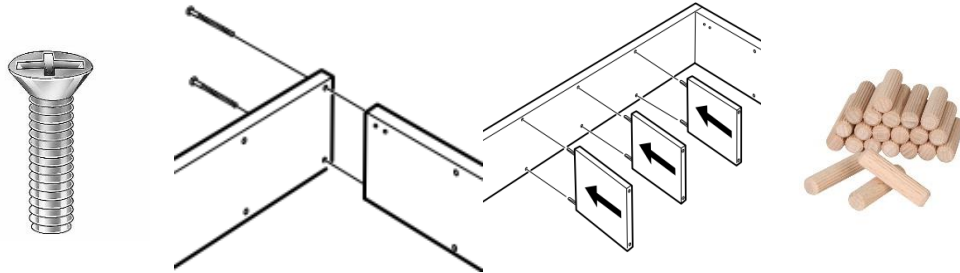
montaje en tornillería (izquierda) montaje con clavijas (derecha) (Fuente IKEA ejemplo)
